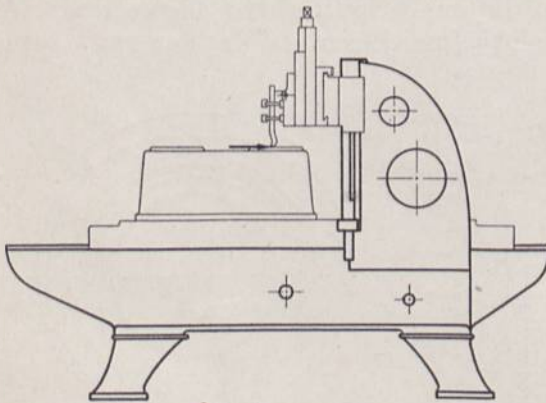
Hobelmaschinenständer mit parabolisch begrenztem Werkzeugträger.
